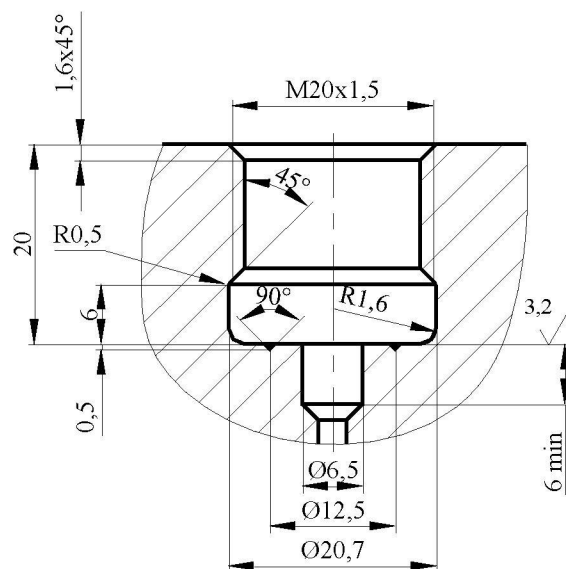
Габаритный чертеж преобразователей СДВ
